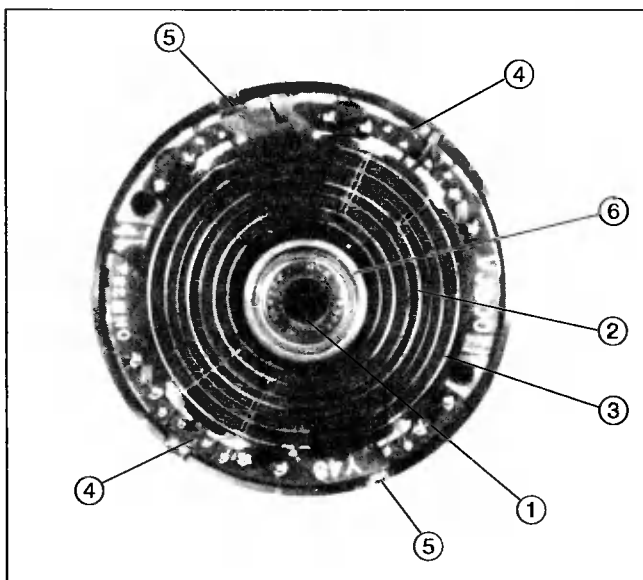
Верхний цилиндр VXP1803 (вид снизу)
